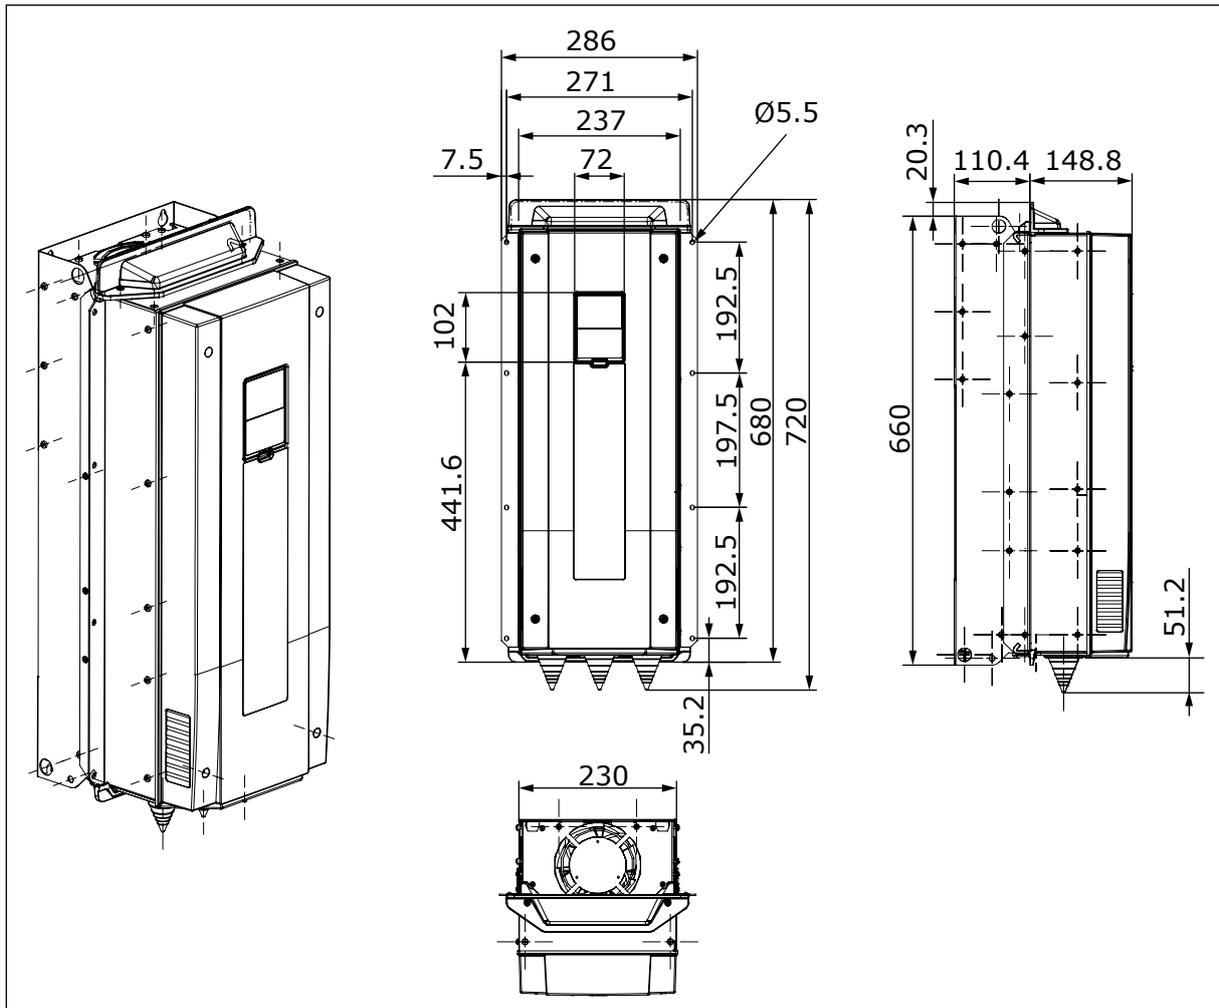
Abmessungen des Frequenzumrichters, Flanschbefestigung, MR7 [mm]
